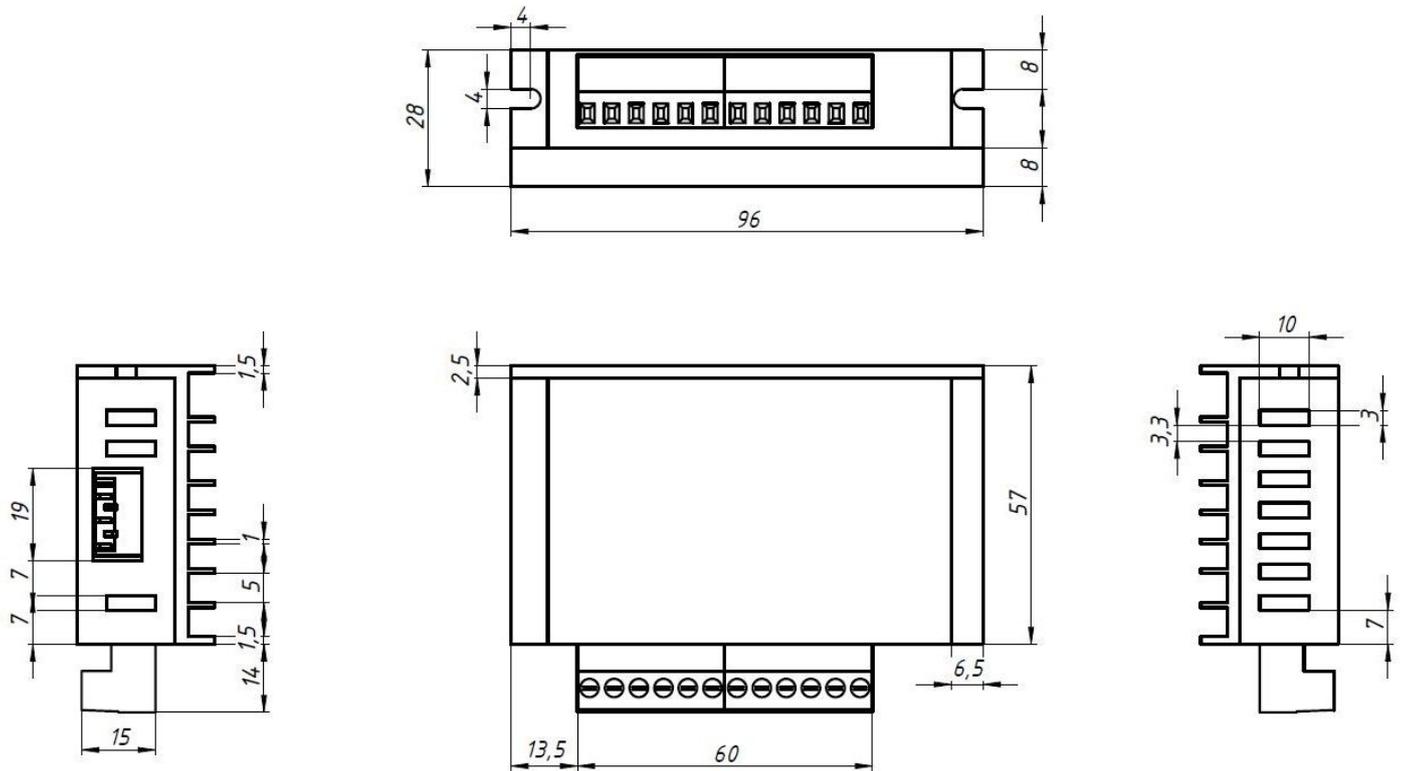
Габаритные размеры и распиновка драйвера TB6600
